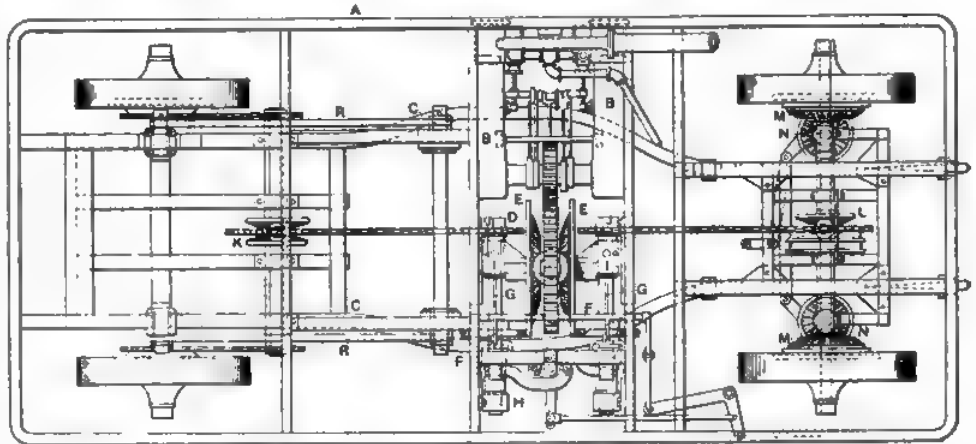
Aultman-Lastwagen: Grundriss.
